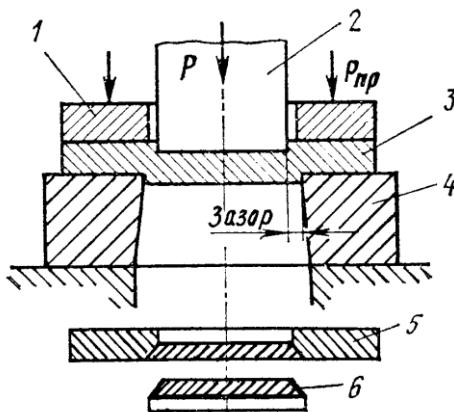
Схема вырубки (пробивки): 1 – прижим; 2 – пуансон; 3 – заготовка; 4 – матрица; 5 – отход (изделие); 6 – изделие (отход);
